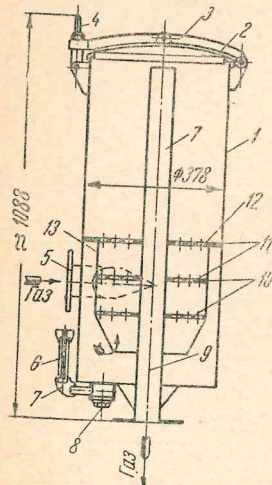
Фильтр тонкой очистки ЦНИИРФ-6
